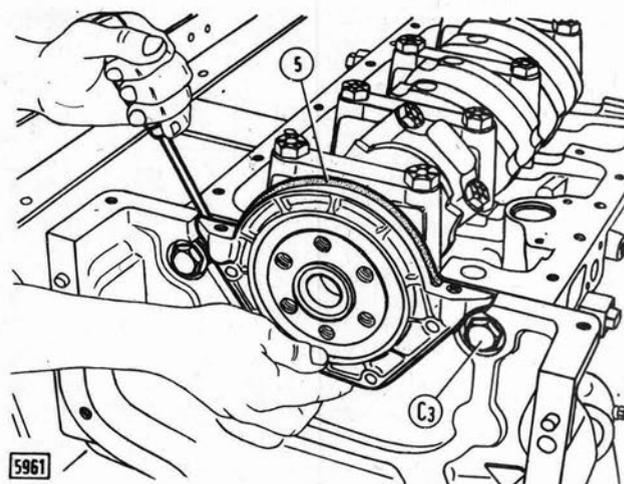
Dépose du joint arrière du vilebrequin.
